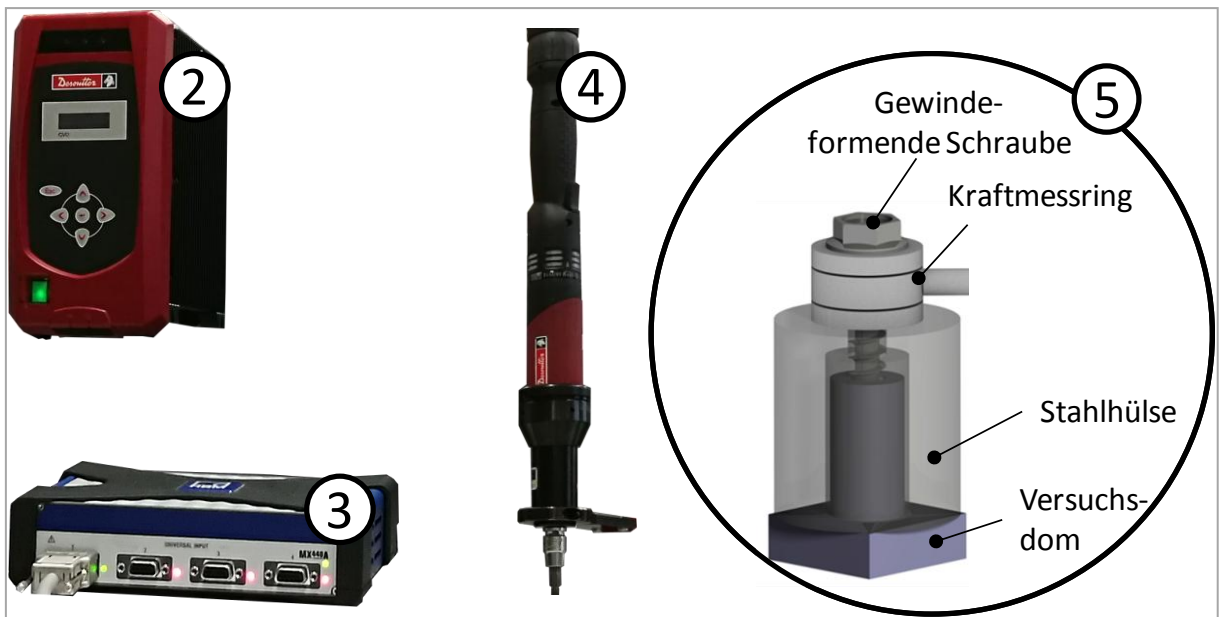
Detaillierte Übersicht der Komponenten des Verschraubungsprüfstands (Teile aus: [26])
